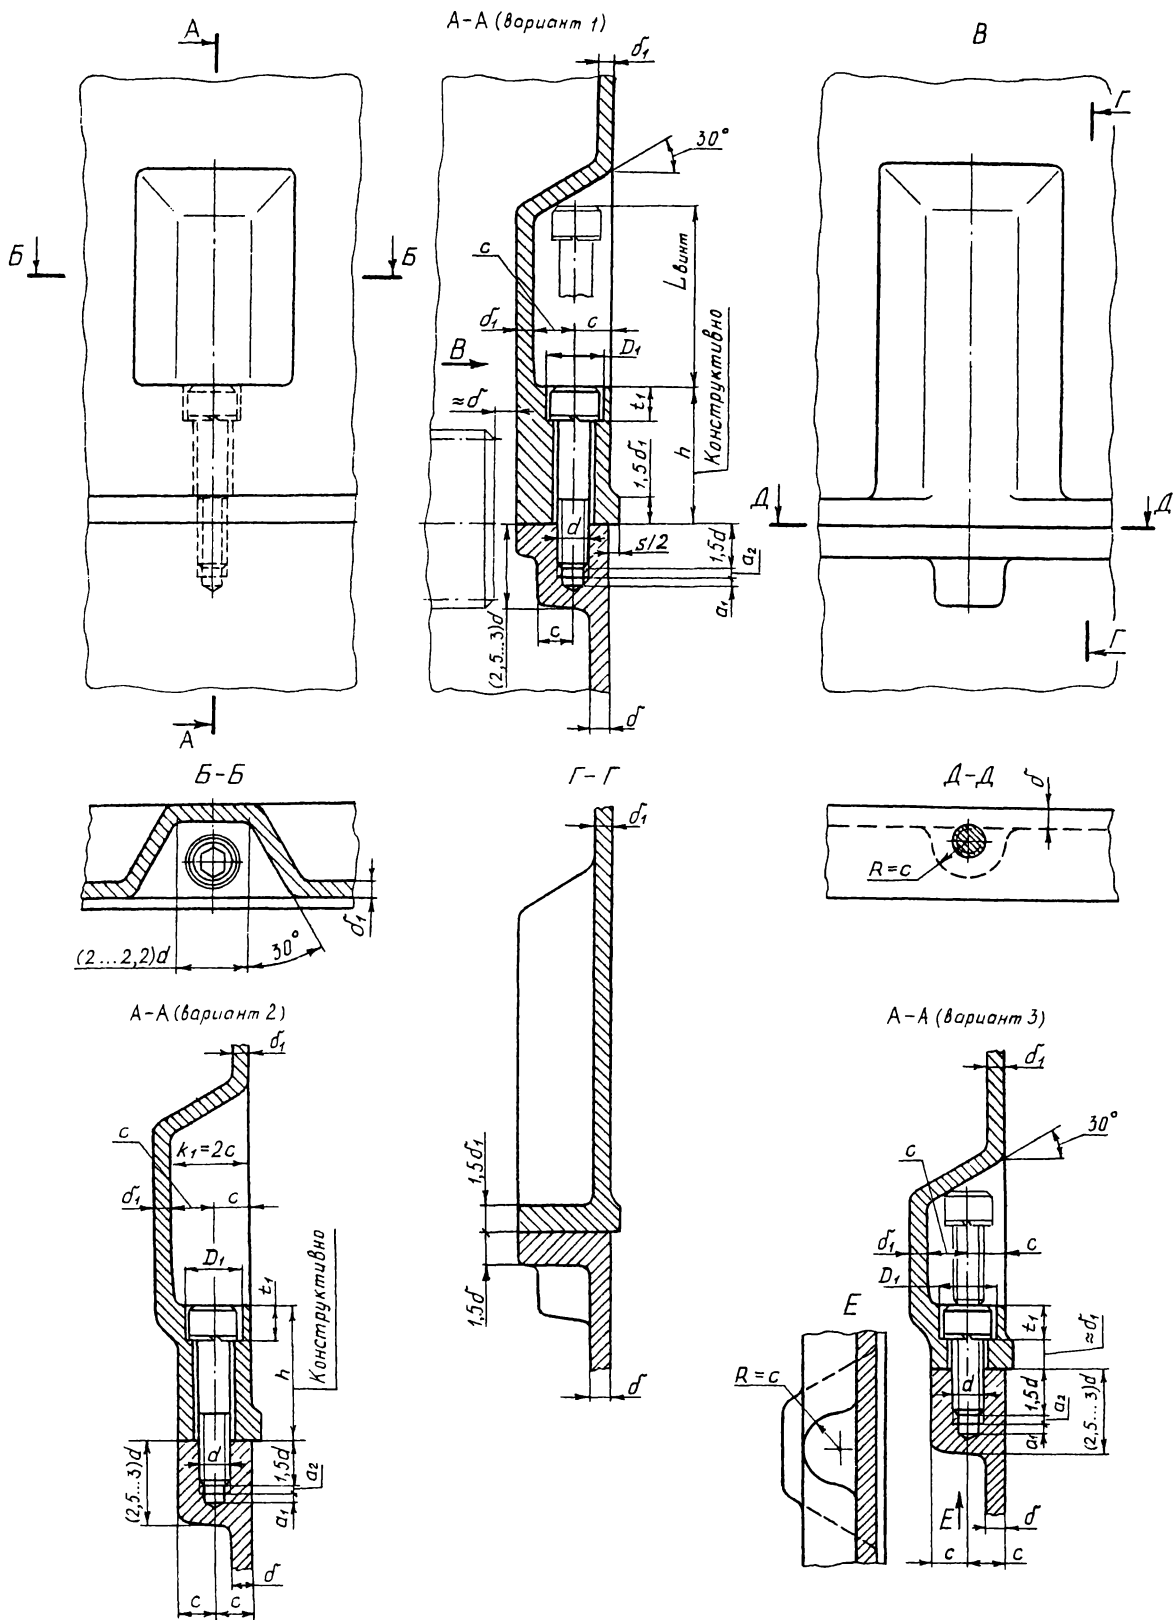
Крепление крышки к корпусу редуктора типа 2
